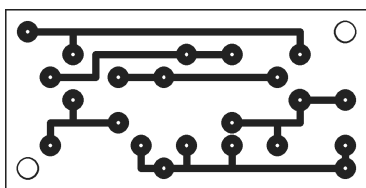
Эскиз платы звукового генератора при её изготовлении с помощью резака. Размер платы: 45x40x1,5 мм
